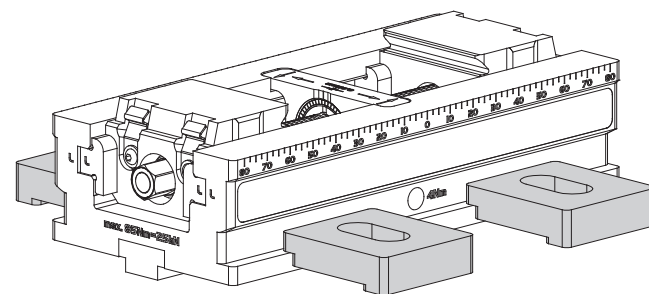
Menghină cu fixare centrică pentru masa mașinii
